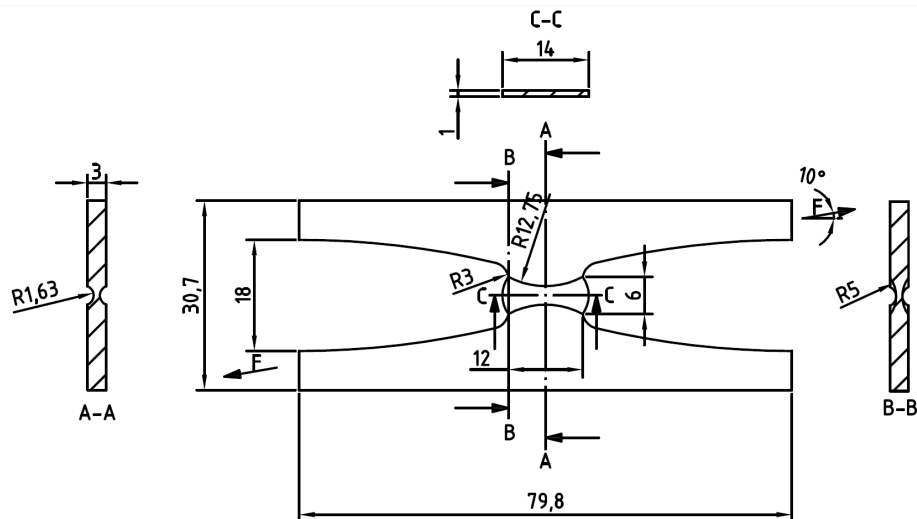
Geometria e direção de carregamento do provete borboleta sob solicitação combinada de tração e corte ($\alpha = 10^\circ$). Dimensões em mm.
